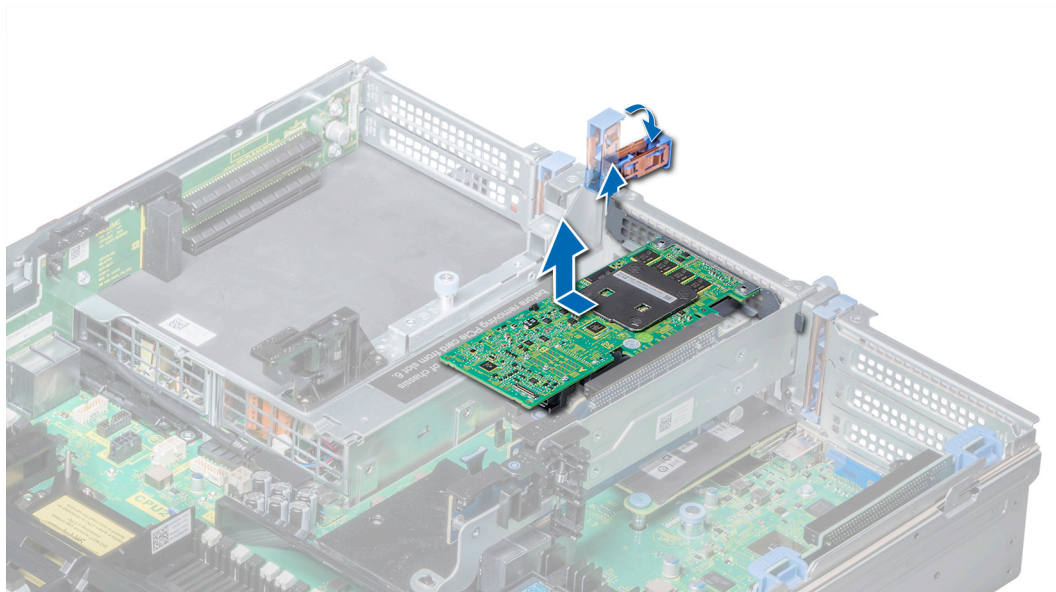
Retrait de la carte d'extension hors de la carte de montage pour cartes d'extension 2
